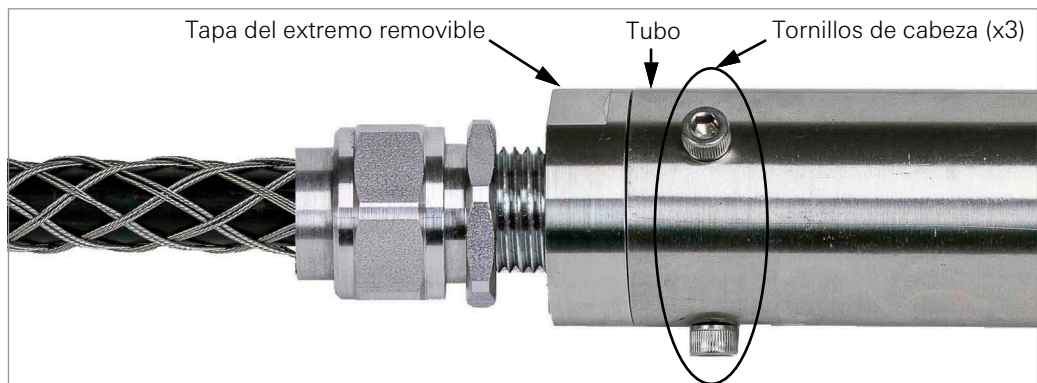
Asegure la tapa del extremo extraíble al tubo
